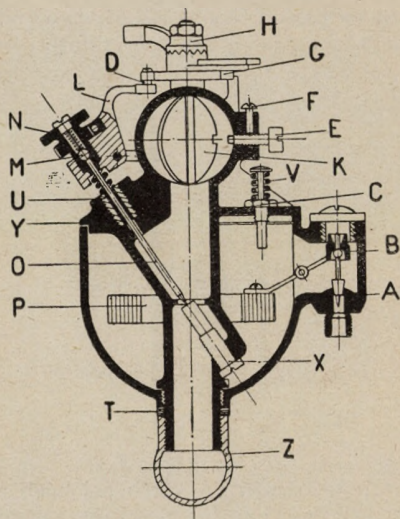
Mechanické brzdění toku benzínu tryskou.
